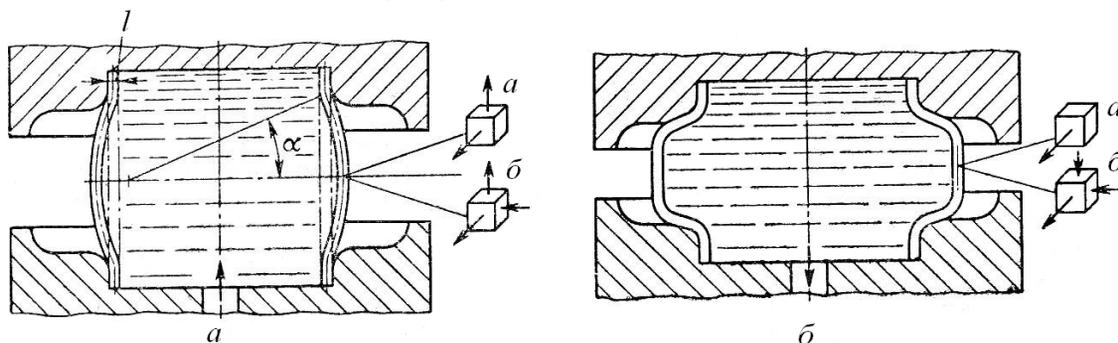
Схемы деформации заготовки при гидравлической формовке гибкого элемента
